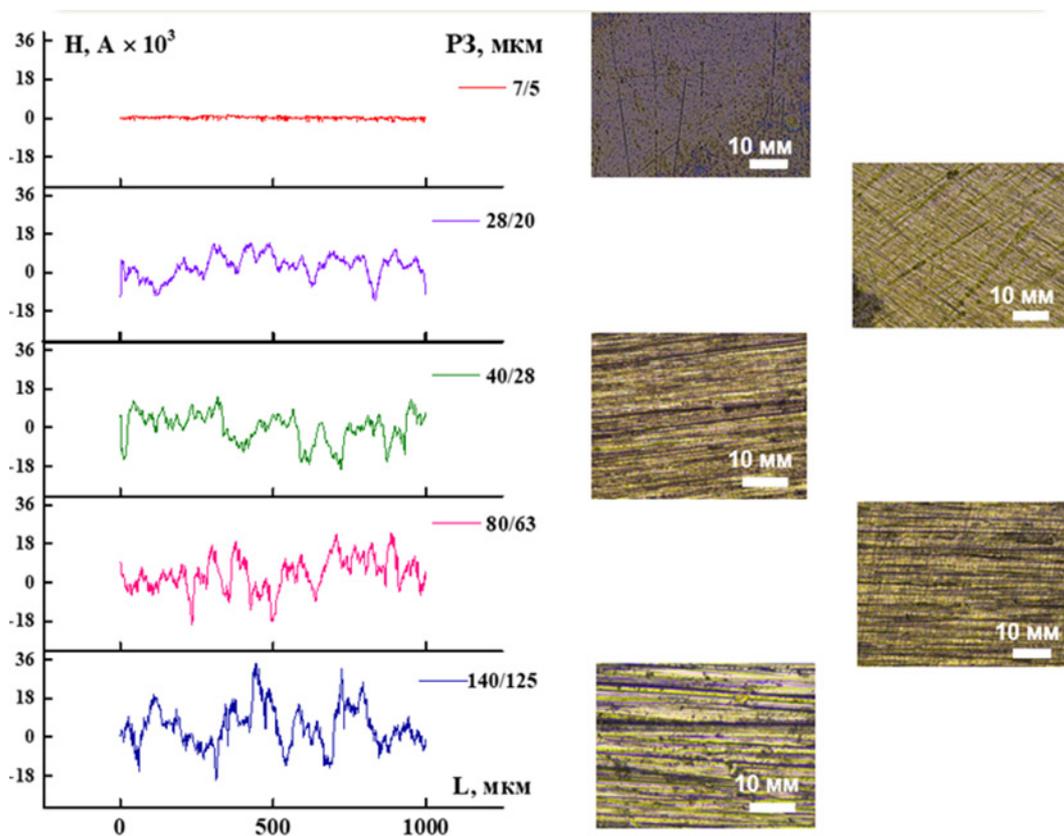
Схема формирования различной степени шероховатости поверхности стали У8А
